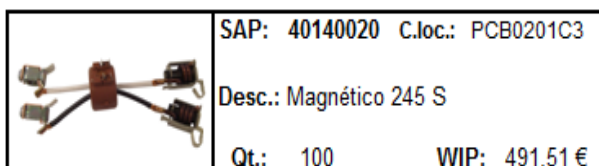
\_ Etiqueta frontal do contentor usado nas soldaduras
